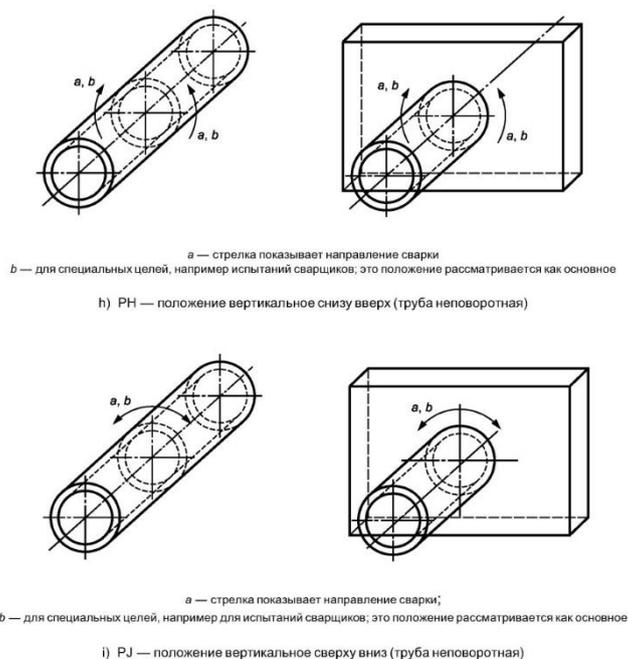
положение вертикальное. *a* – стрелка указывает положение при сварке.
